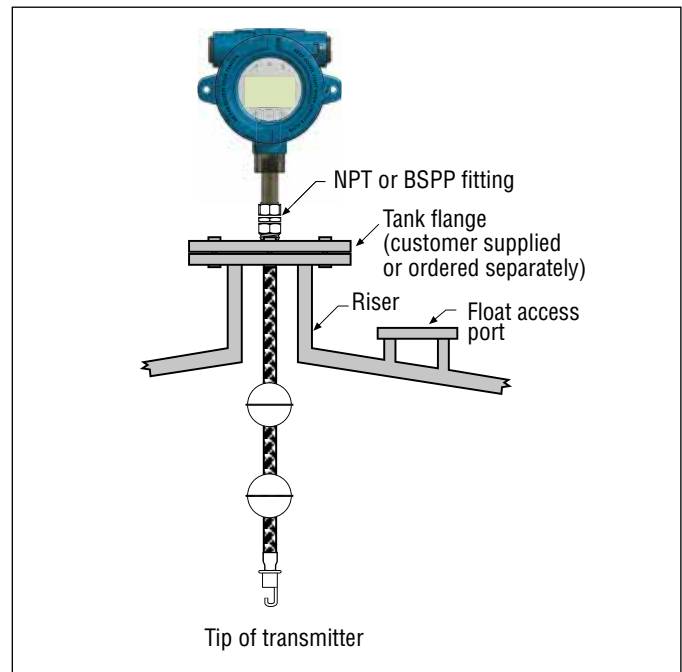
Montage mit Gewindeflansch für flexiblen Schlauch
